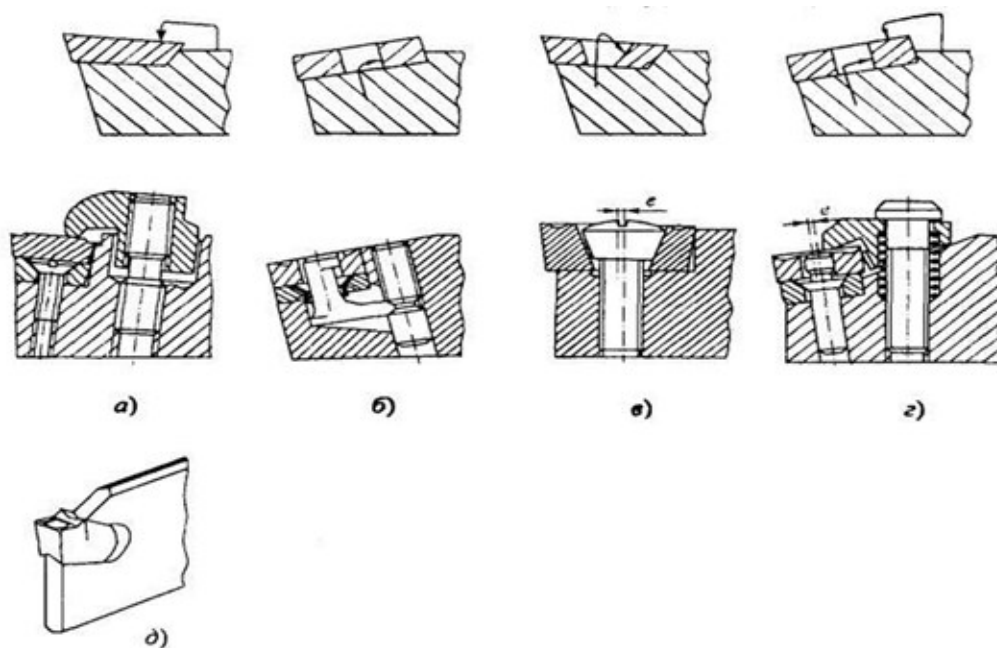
Схемы механического крепления твердосплавных СМП:
